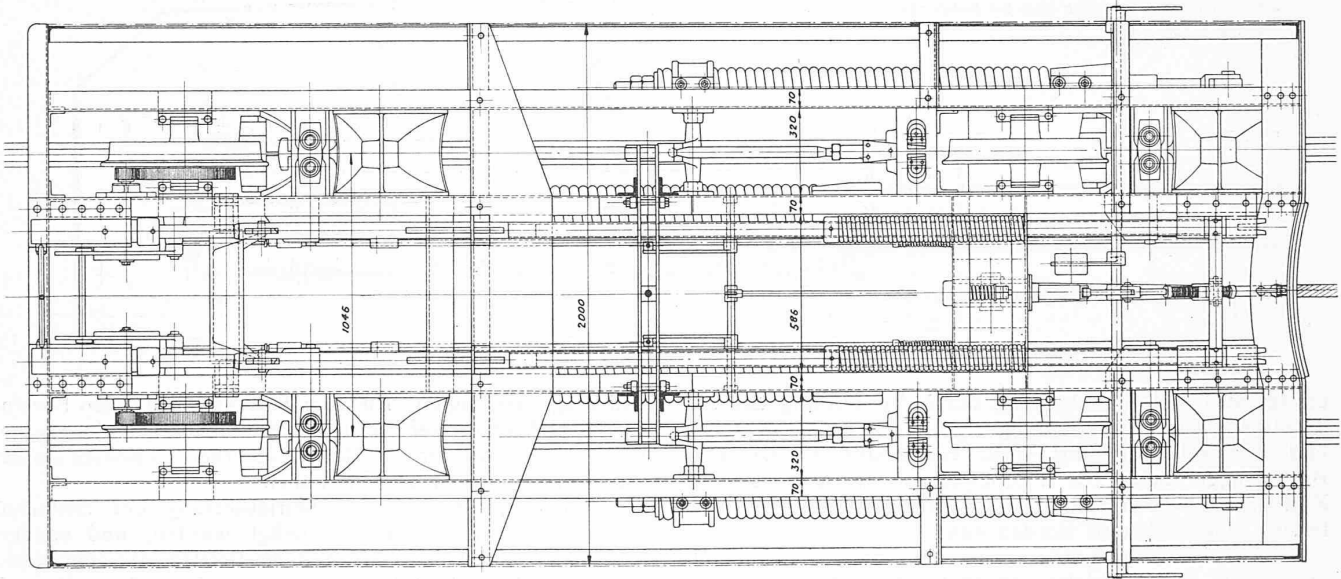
Grundriss des Untergestells des Bremswagens der Seilbahn Triest-Opcina. — Masstab 1 : 25.
